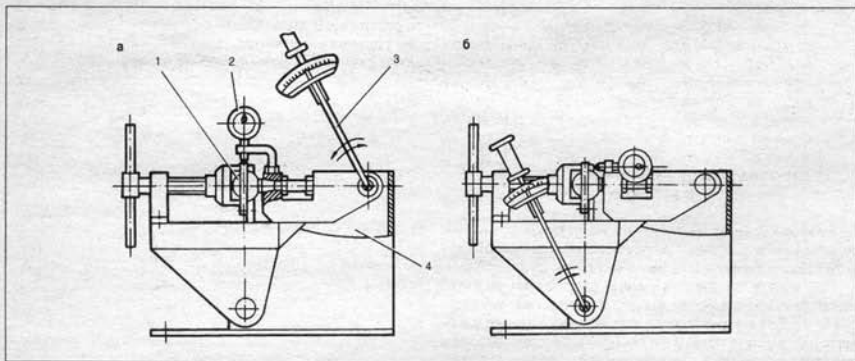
Проверка шарового шарнира на приспособлении 02.8701.9502:
